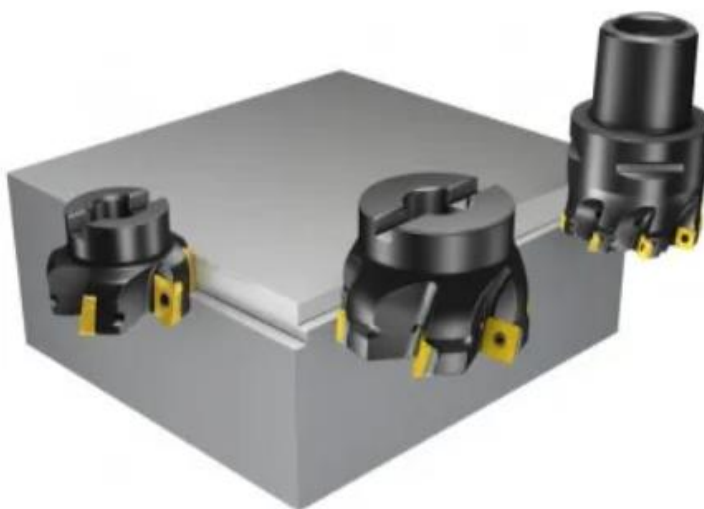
Фрезерування неглибоких уступів[8]
